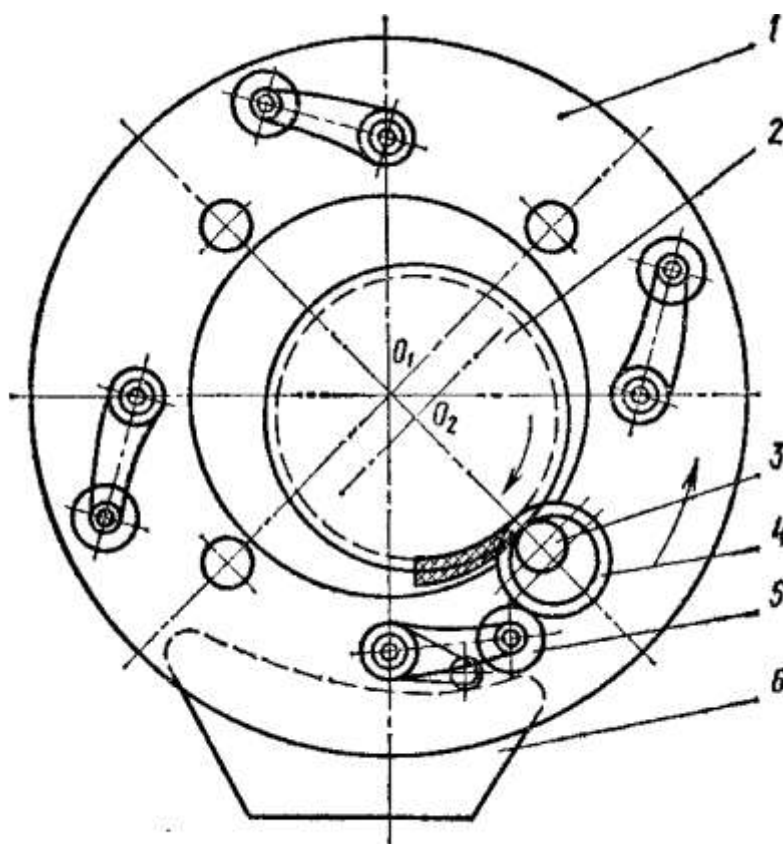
Схема кольцеракатного стана типа MERW
